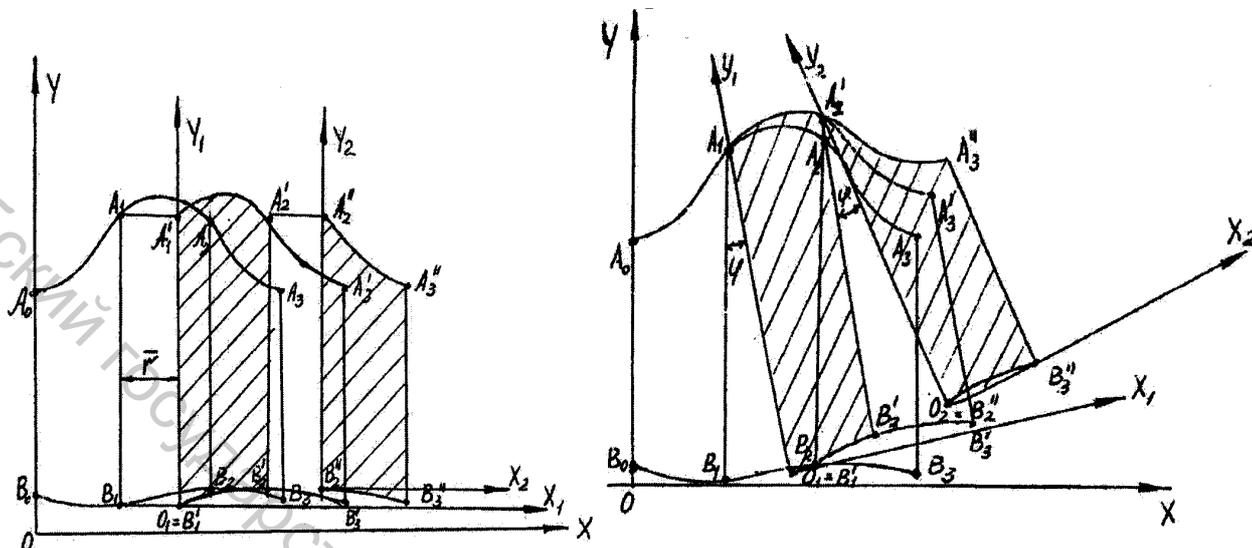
Виды смещений при КДМБК деталей конструкции
